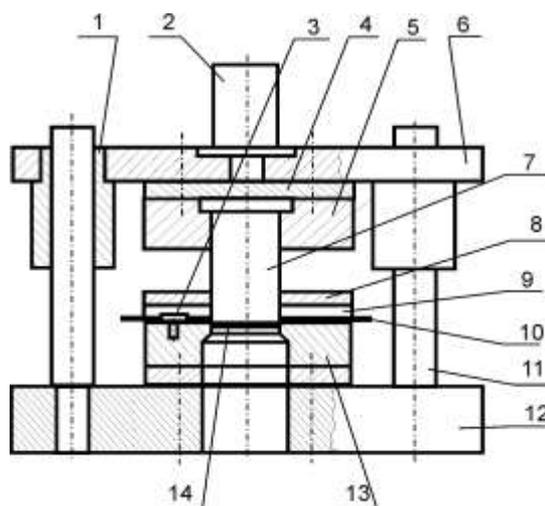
Конструкція штампа для пробивання отворів: 1 – направляюча втулка; 2 – хвостовик; 3 – фіксатор; 4 – плита підкладна; 5 – пуансонотримач; 6 – плита верхня; 7 – пуансон; 8 – знімач; 9 – направляюча лінійка; 10 – заготовка; 11 – колонка; 12 – плита нижня; 13 – матриця; 14 – виштамповка
